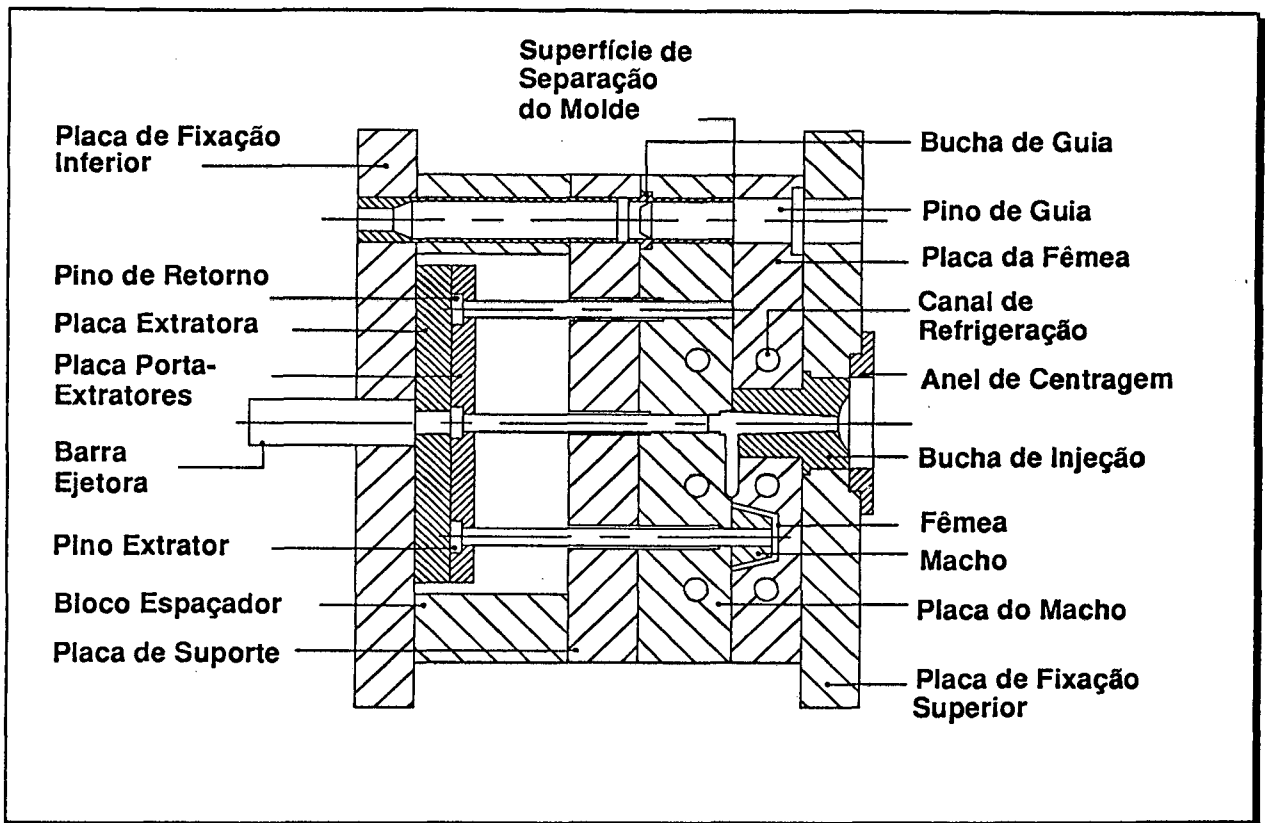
Representação dos componentes básicos de um molde do tipo "Standard" [12].
